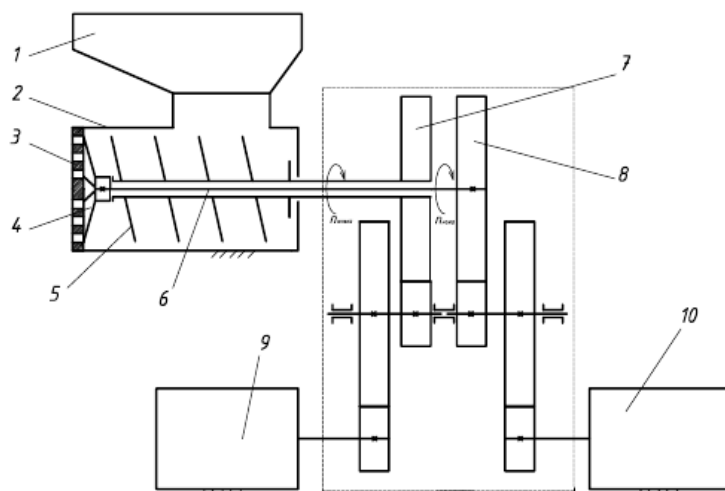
Кінематична схема м'ясорубки з роздільними приводами ножа і шнека:
